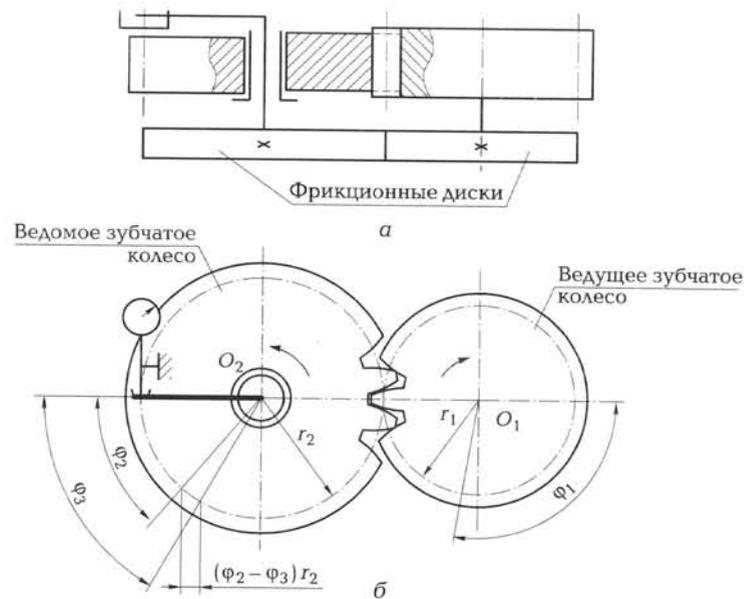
Схема комплексного контроля цилиндрической зубчатой передачи:
